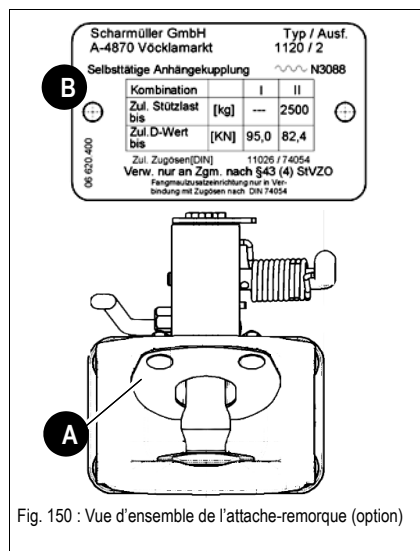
Vue d'ensemble de l'attache-remorque (option)
